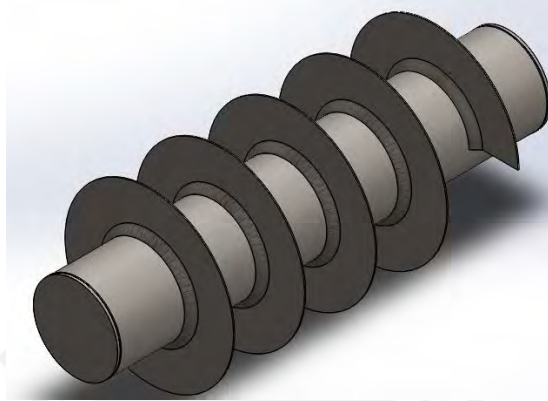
Secciones circulares equivalentes a la hélice con soldadura.
